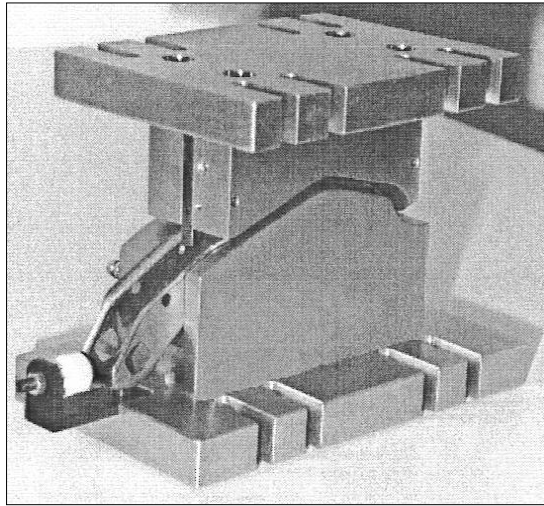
Detalle del montaje de un dispositivo de soldadura por proyección en la mesa de la prensa.
